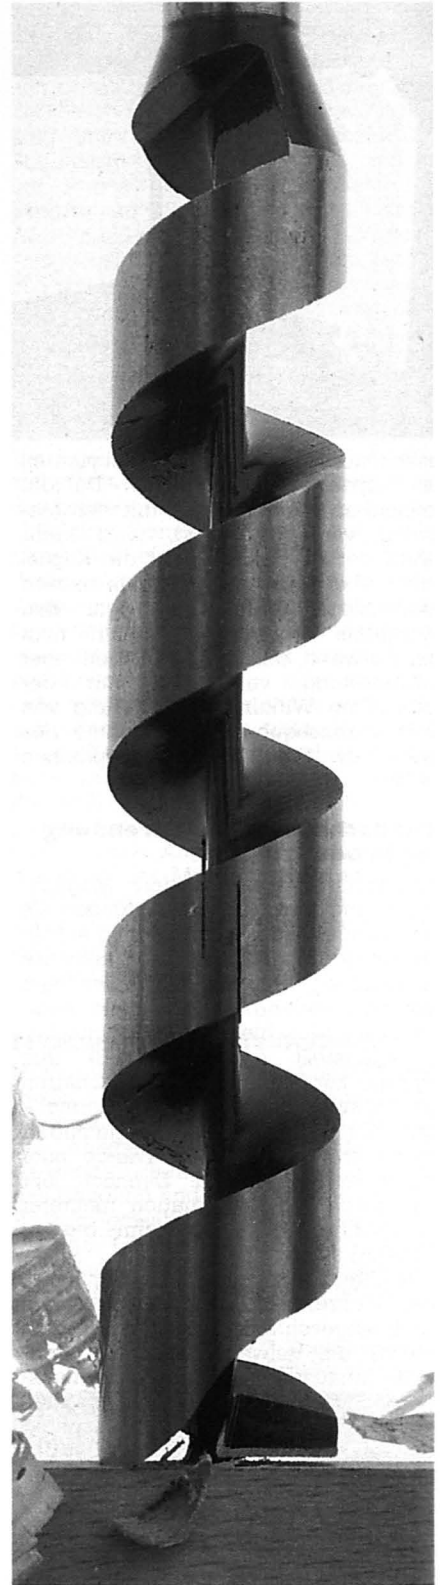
Bohrwerkzeug (Wendelbohrer)
